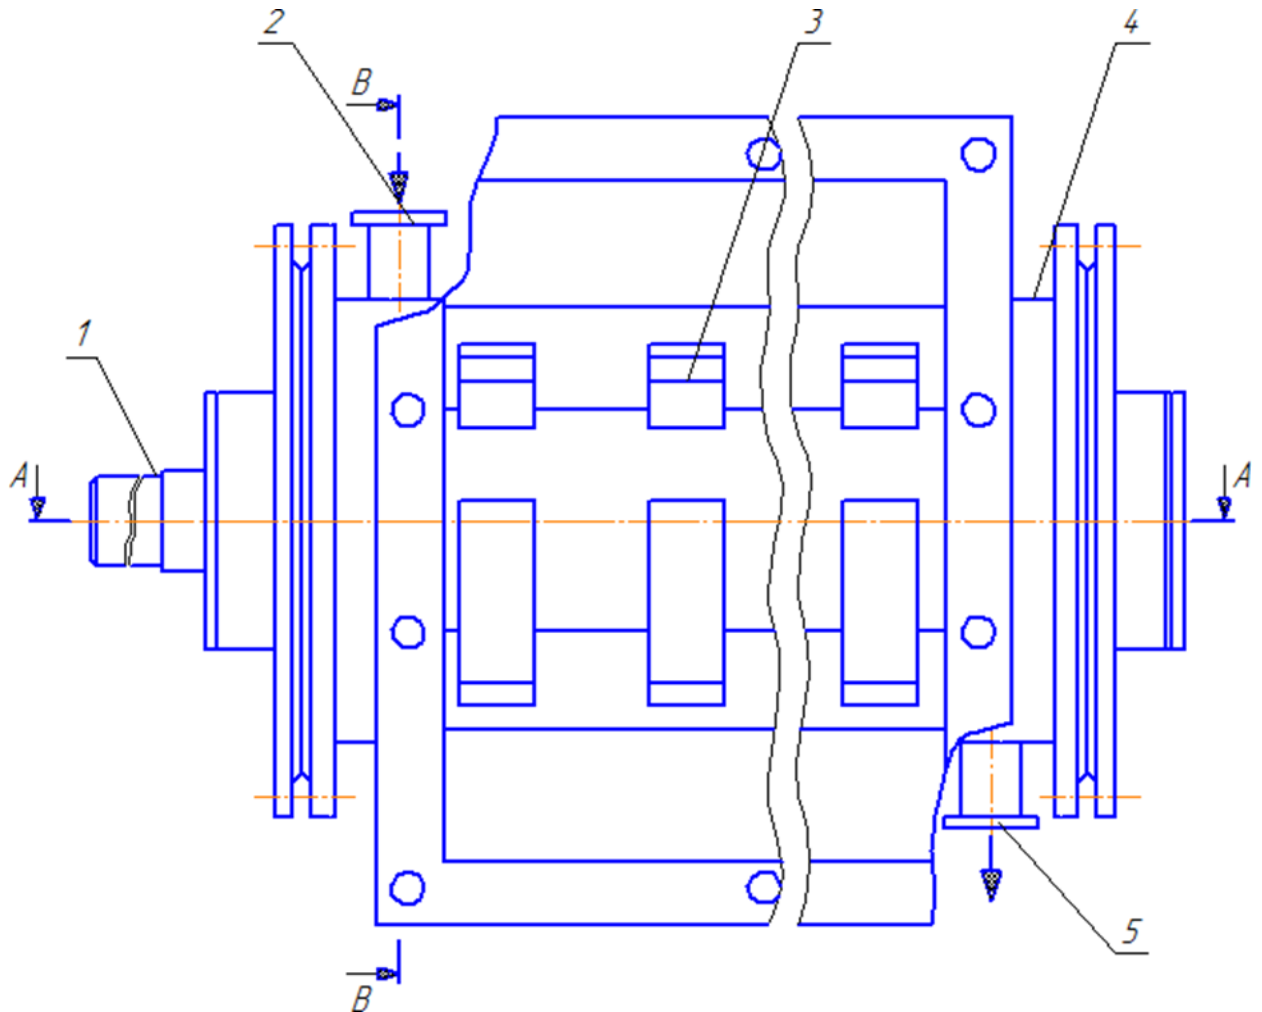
Модернізований завантажувальний пристрій 1 – вал; 2-патрубок; 3–лопаті із фторопласту; 4 – корпус; Завантажувальний вал 1 розміщений на підшипникових опорах 10 та 13 (рис. 3.2). Корпус 7 закривається з обох боків за допомогою кришок 6.
